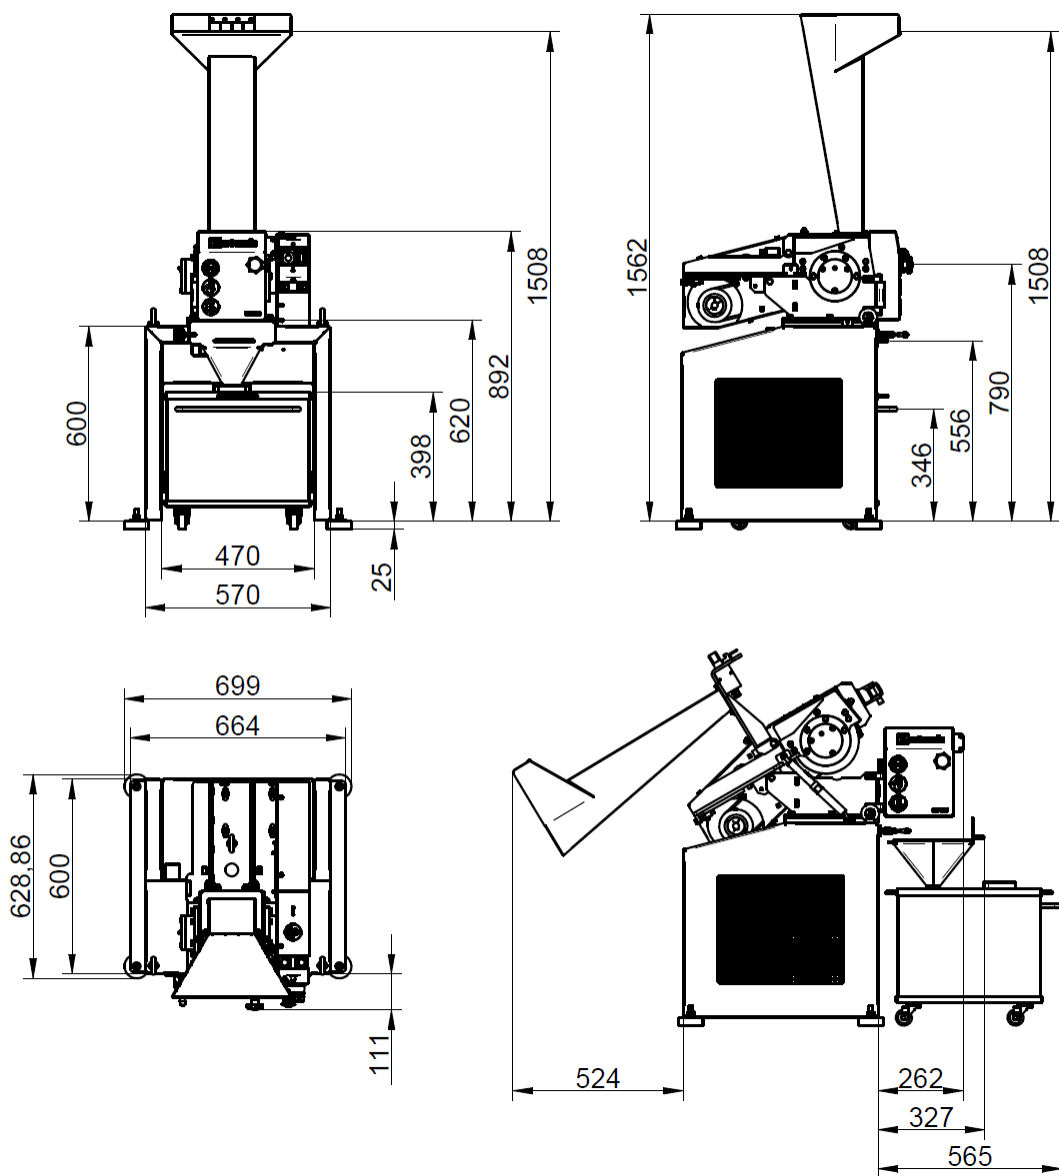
монтажный чертеж Загрузочная воронка для длинномерного материала
